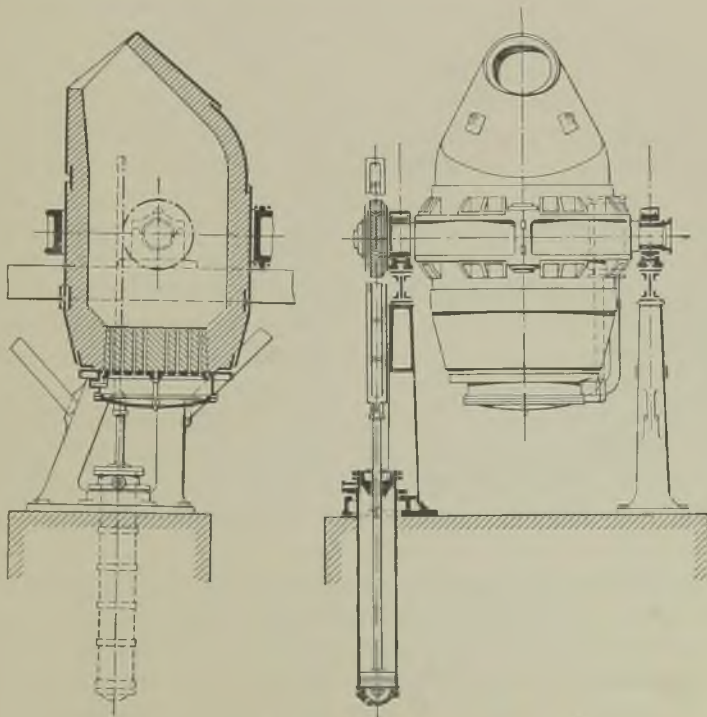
Bessemerbirne in Schnitt und Ansicht.
